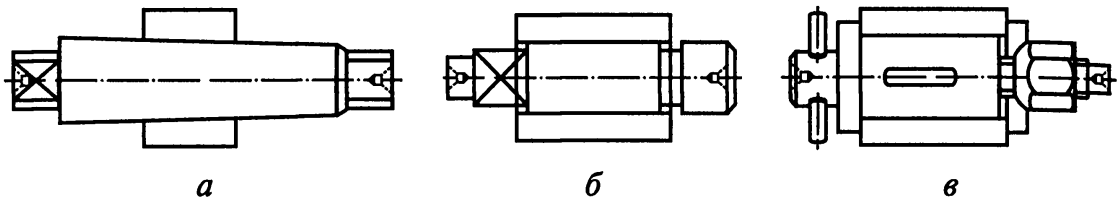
Жесткие оправки, на которые детали насаживаются: *а* — с цилиндрическими отверстиями; *б* — с натягом; *в* — с зазором
